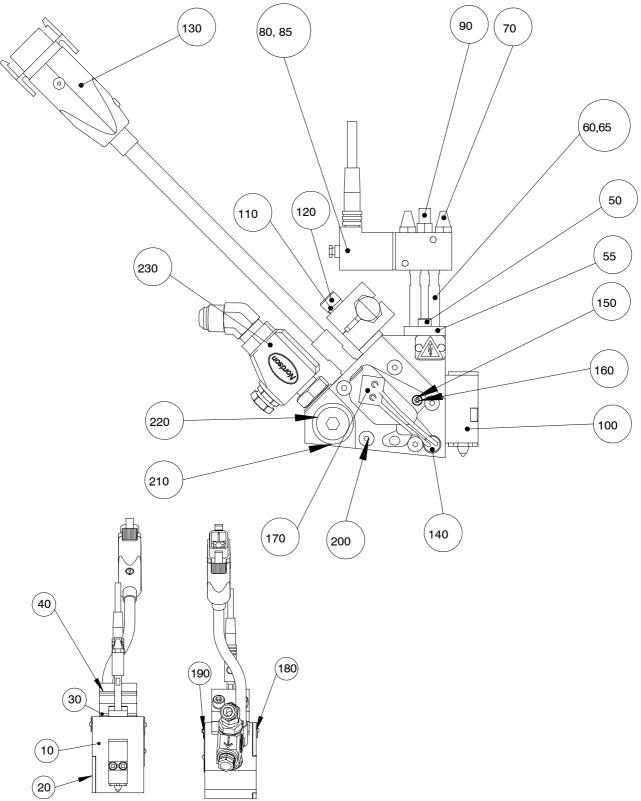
Pistolet mono-module configurable, pièces d'une électrovanne SD
